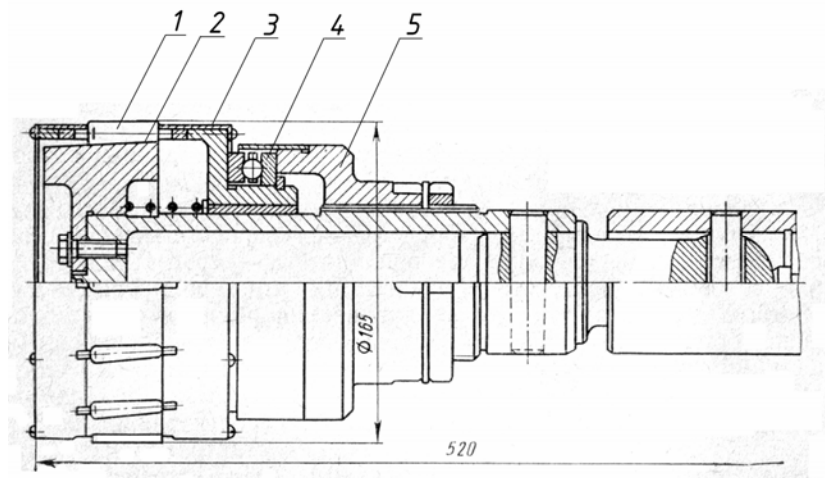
Планетарная роликовая головка для раскатывания отверстий
